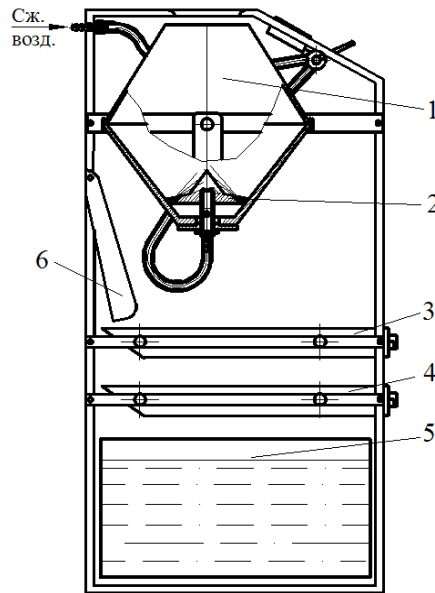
Установка с объемом рабочей камеры 30 л: 1 – рабочая камера; 2 – сопловой аппарат (завихритель); 3 – решето для деталей; 4 – решето для абразивного зерна; 5 – бак-отстойник; 6 – желоб для суспензии
